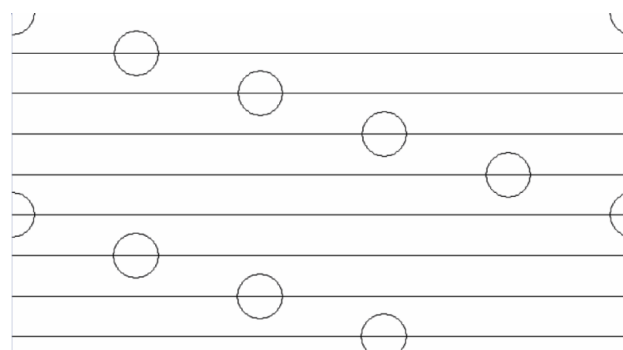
Расположение ножей на фрезе фрезера МТФ-12А
